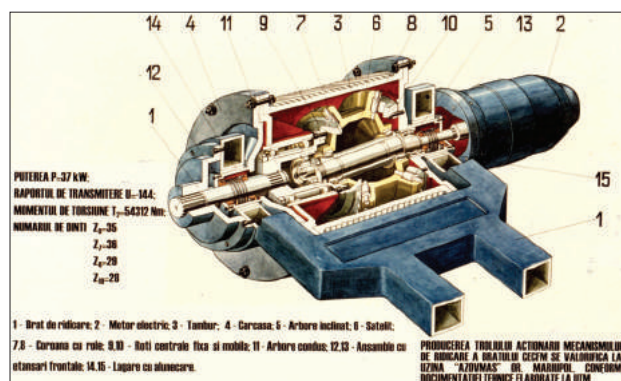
Mecanism de acționare a tamburului Complexului Robotizat cu reductor precesional 2K-H
